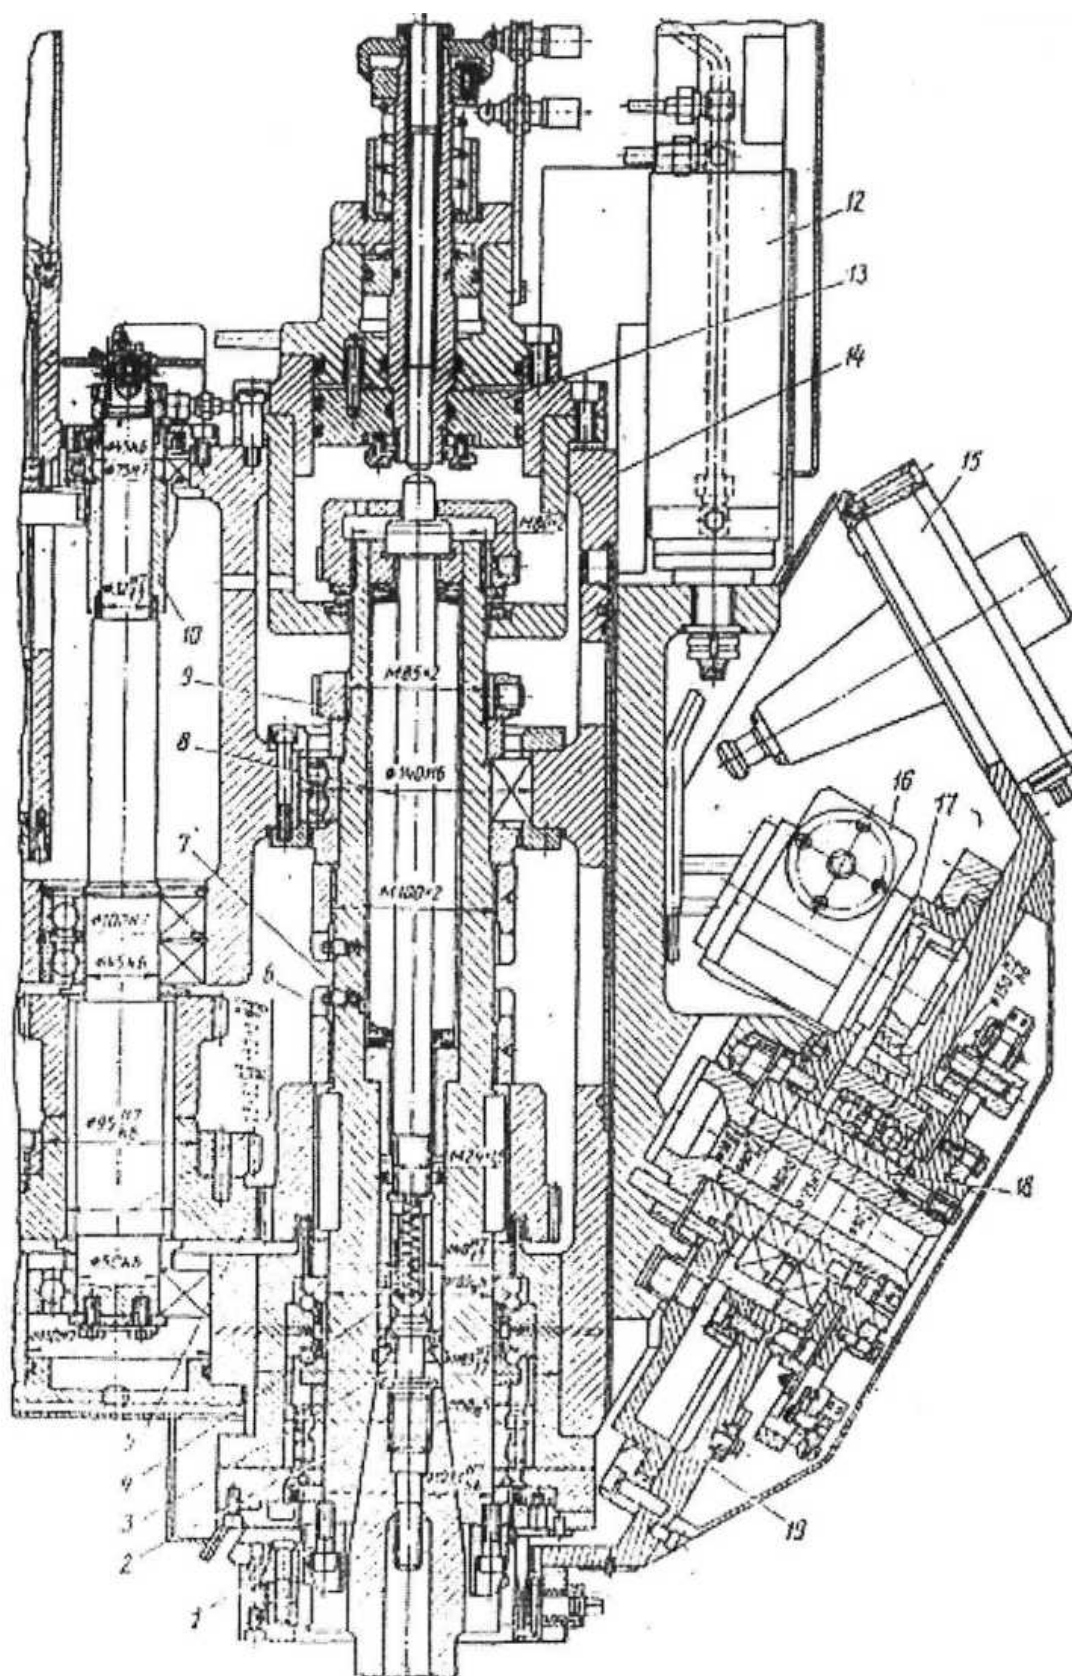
17. Механізм автоматичної зміни інструментів для вертикаль – фрезерного верстата з ЧПК.
